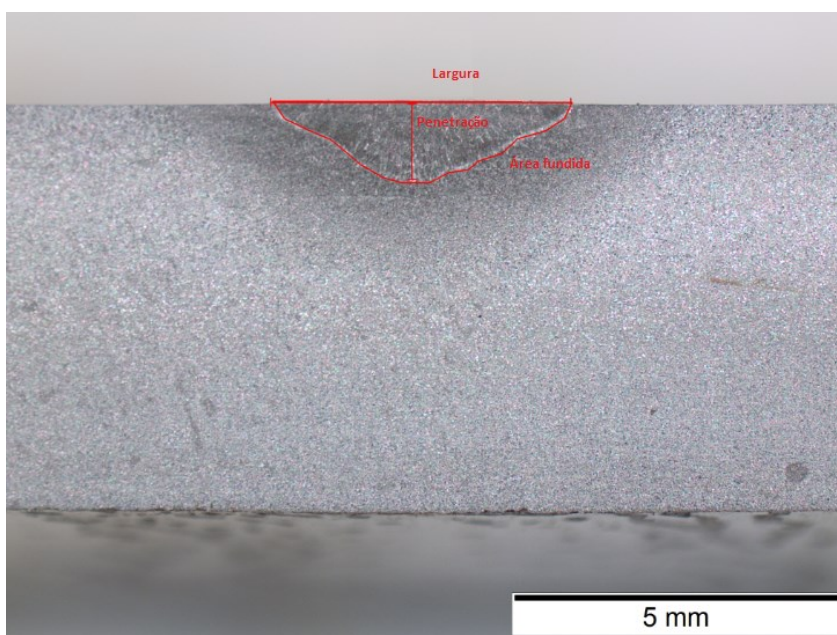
Geometria do cordão de solda (LAPROSOLDA FEMEC UFU).
